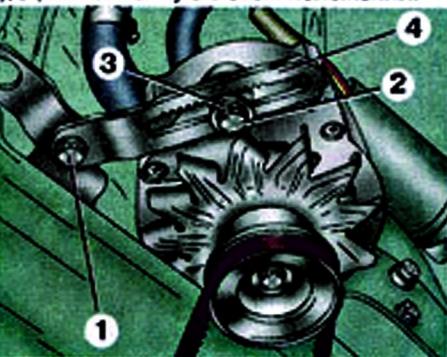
Механизм натяжения ремня привода генератора: 1 — болт крепления кронштейна; 2 — болт механизма натяжения; 3 — гайка регулировочная механизма натяжения; 4 — кронштейн механизма натяжения
